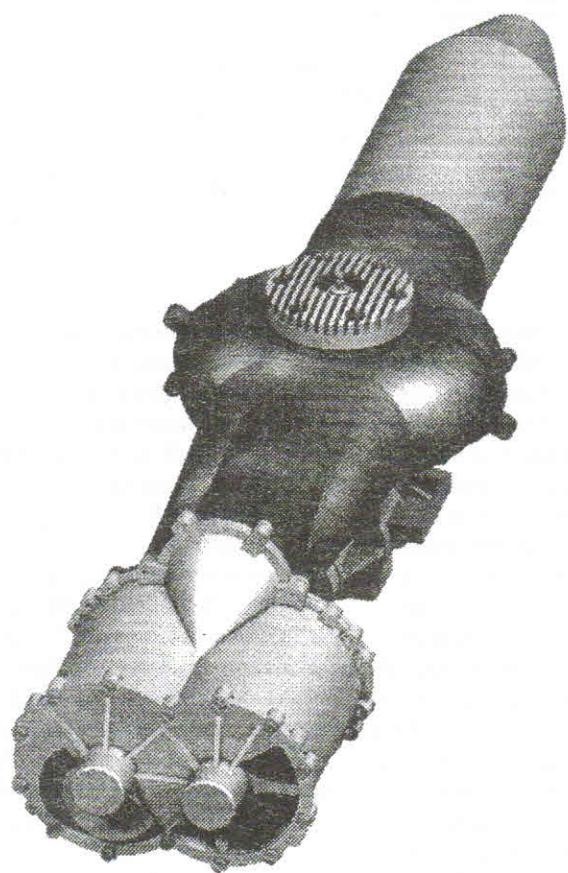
Внешний вид МкВРД с винтовым компрессором и форсажной камерой
